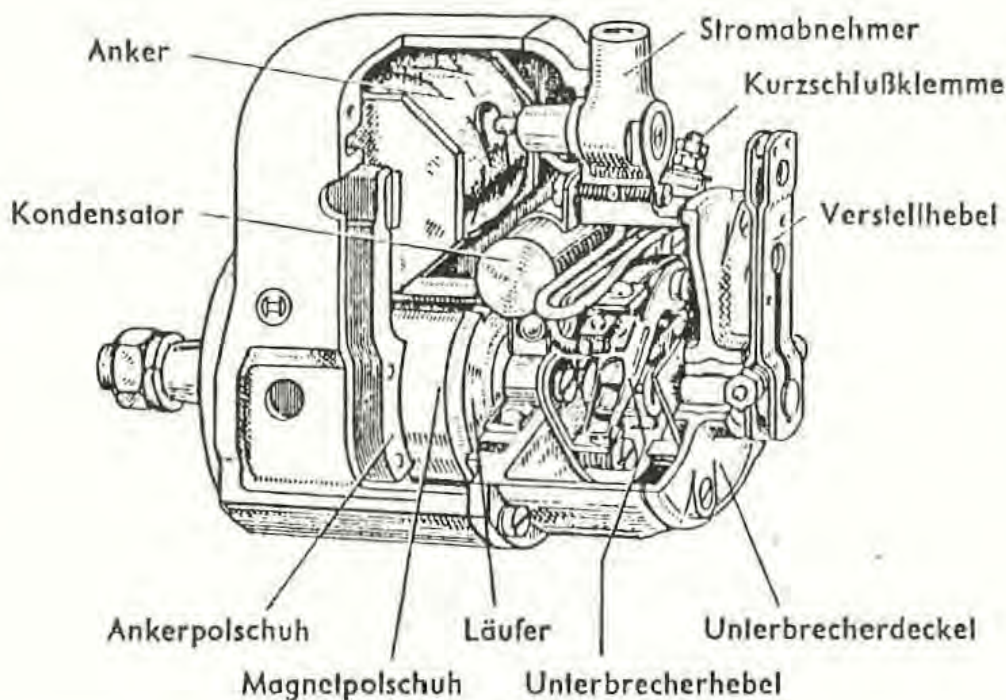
Bosch-Magnetzünder Type MZ/JF 1 für Einzylindermotor — Schnittbild
